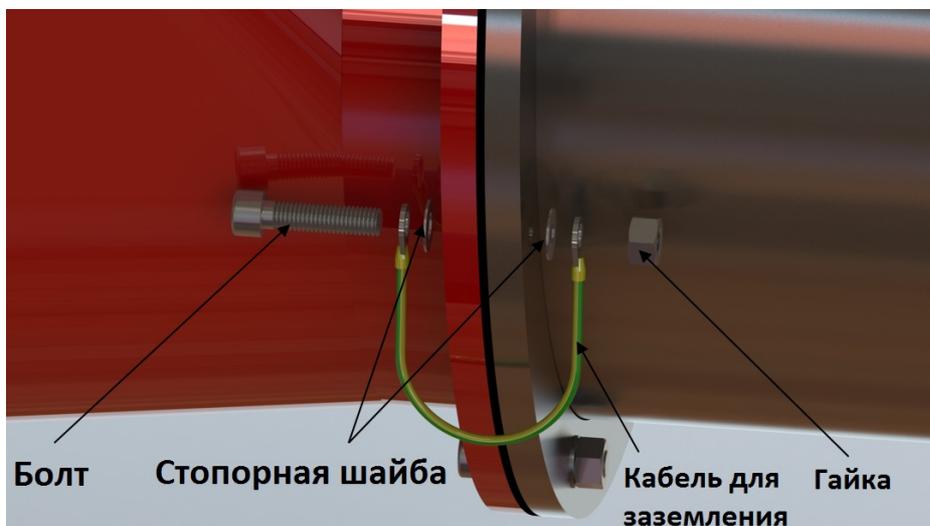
Электропроводное соединение с помощью кабеля заземления
